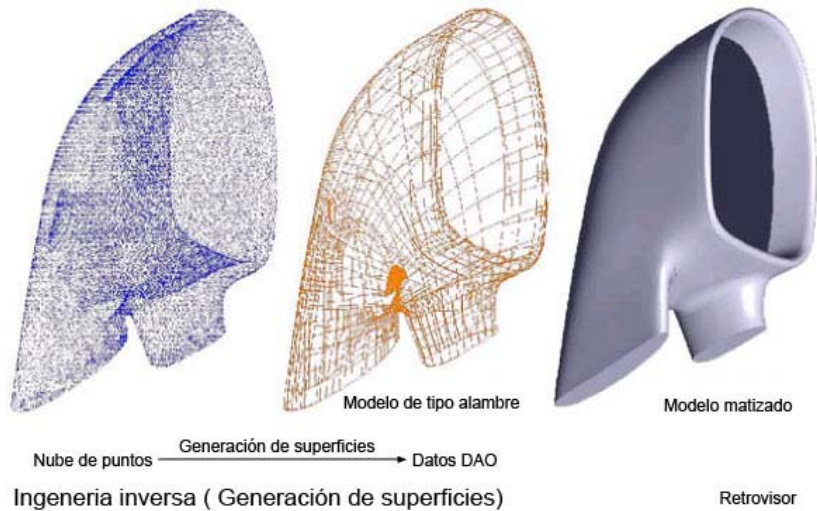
Reconstrucción 3D para ingeniería inversa.
